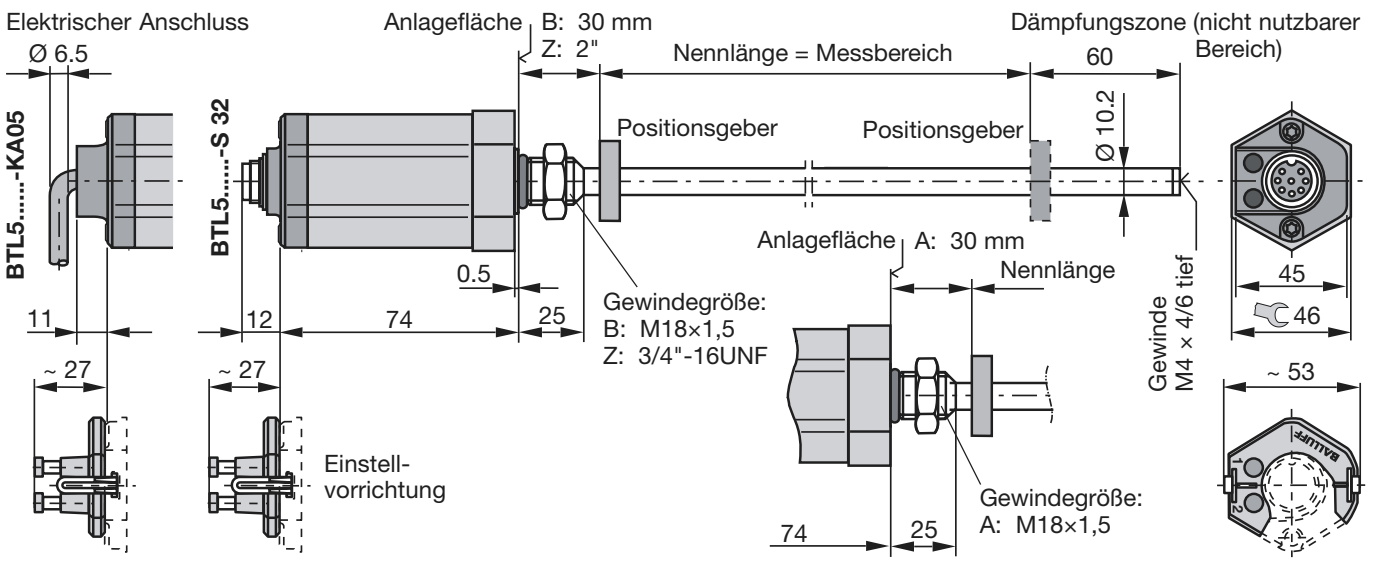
Wegaufnehmer BTL5...A/B/Z..., Maßzeichnung
